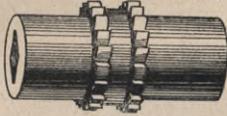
Stecknuß zum „Rapid“-Schraubenschlüssel für tiefliegende Muttern.
